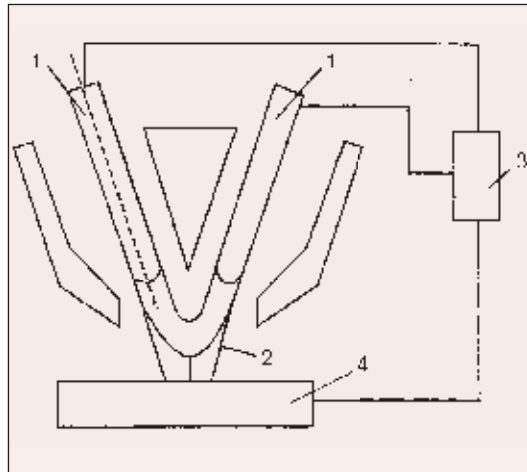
Схема плазменной сварки трехфазной дугой: 1 — электроды; 2 — дуги прямого и косвенного действия; 3 — источник питания; 4 — изделие
